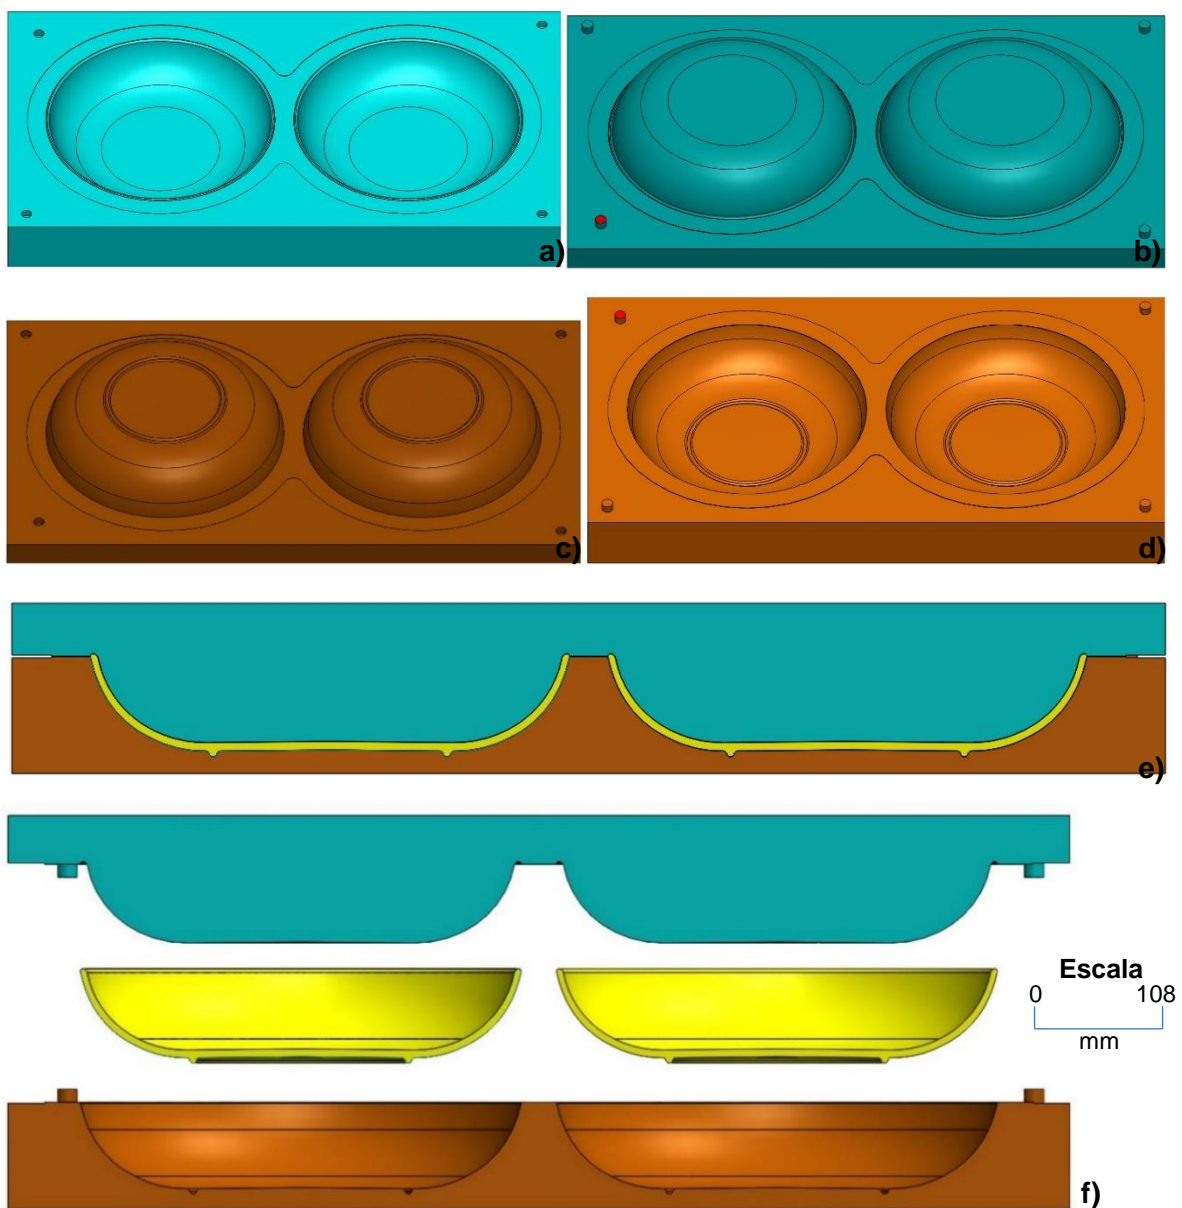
Componentes necessários para a conformação por enchimento sob pressão da tigela grande: a) e c) madres; b) e d) moldes; e) e f) montagem CAD dos moldes e da tigela.
